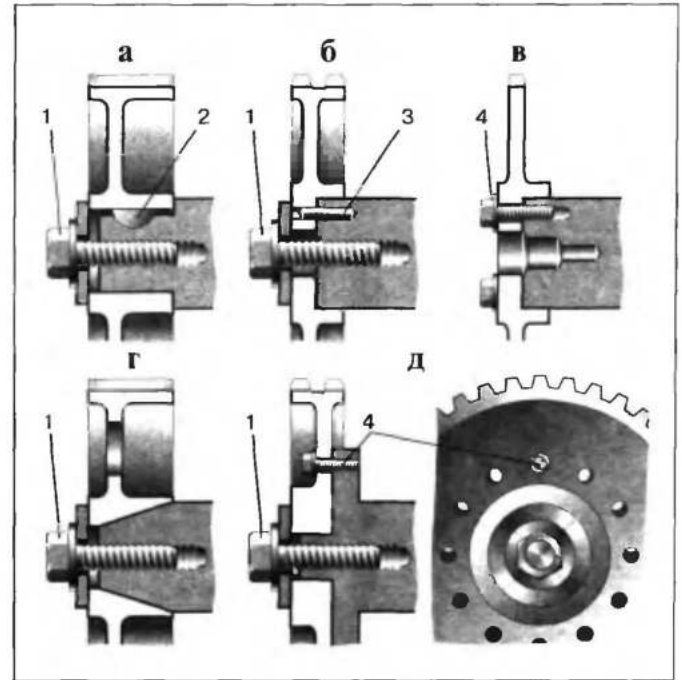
Крепление колес привода на распределительных валах: а — с помощью болта и шпонки; б — с помощью болта и штифта; в — тремя-четырьмя болтами по фланцу; г — посадкой колеса на конус и болтом; д — с помощью двух болтов — центрального и установочного (колесо имеет на одно отверстие для установочного болта больше или меньше, чем распределительный вал); 1 — центральный болт; 2 — шпонка; 3 — штифт; 4 — установочный болт
